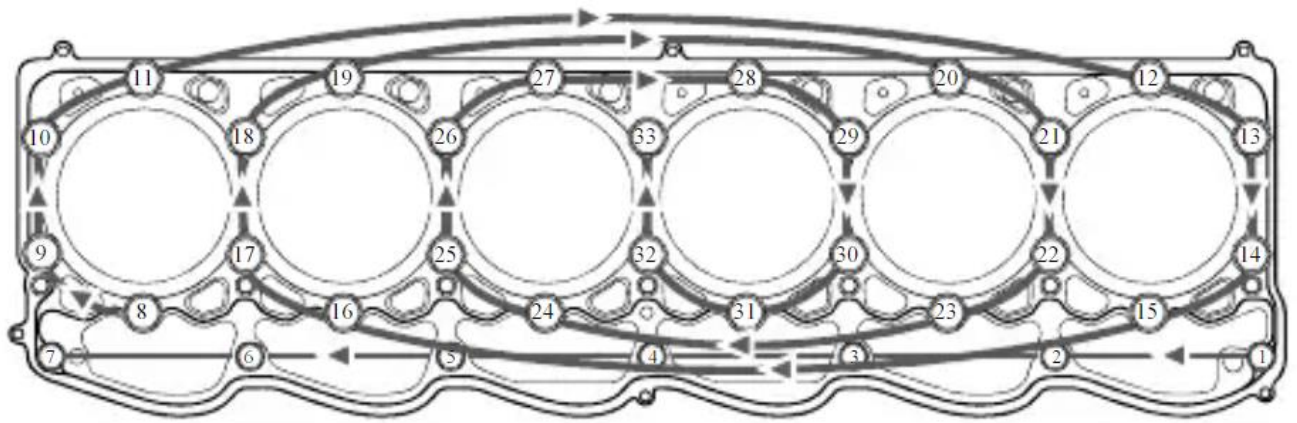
Порядок відкручування болтів кріплення ГБЦ
